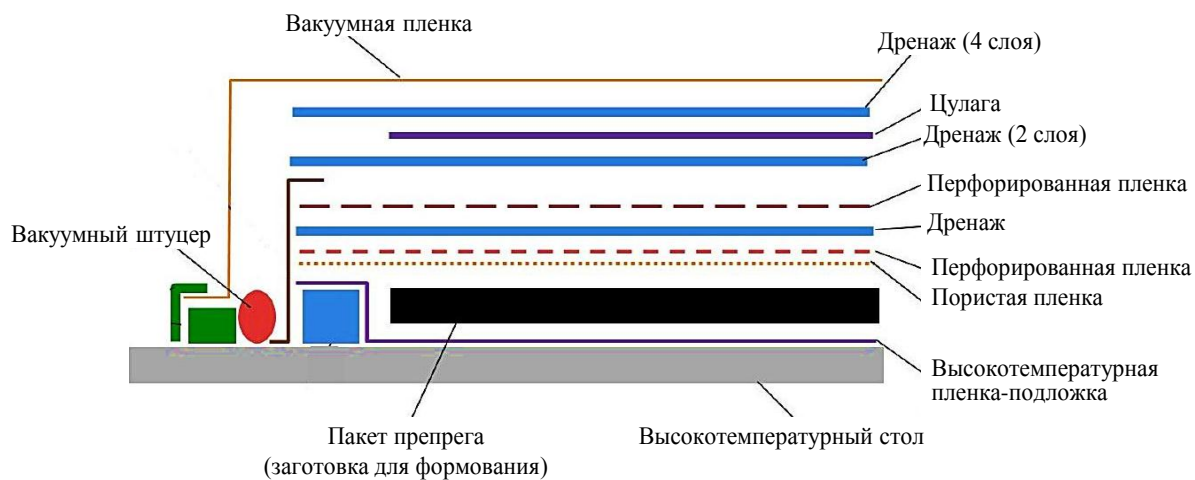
Схема сборки пакета для автоклавного формования углепластика [24]
